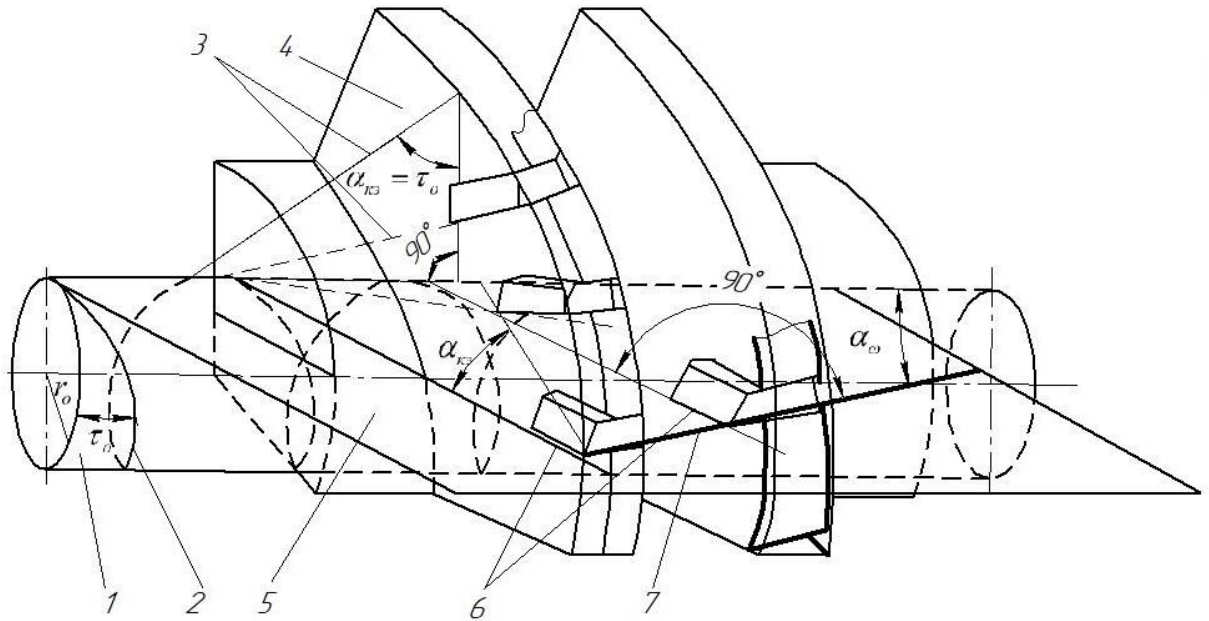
Геометрія правого корпусу правозахідної евольвентної фрези з роздільною схемою формоутворення: 1 - основний циліндр; 2 - напрямна гвинтова лінія; 3 – утворюючі прямі (ОП); 4 – ліва гвинтова поверхня; 5 – площина верстатного зачеплення; 6 – різальні кромки зубів, розташовані на гвинтовій евольвентній поверхні; 7 - лінія верстатного зачеплення
